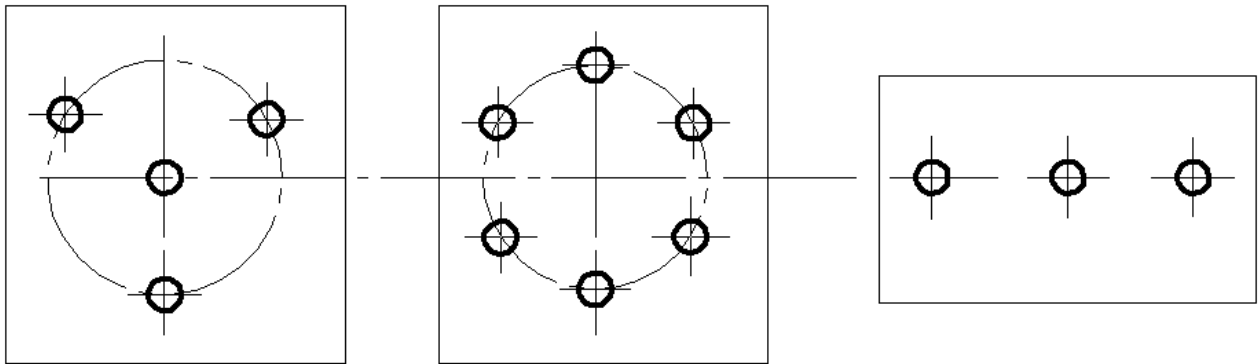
Схеми розташування отворів, які обробляють з використанням багатошпindelних свердлильних головок
